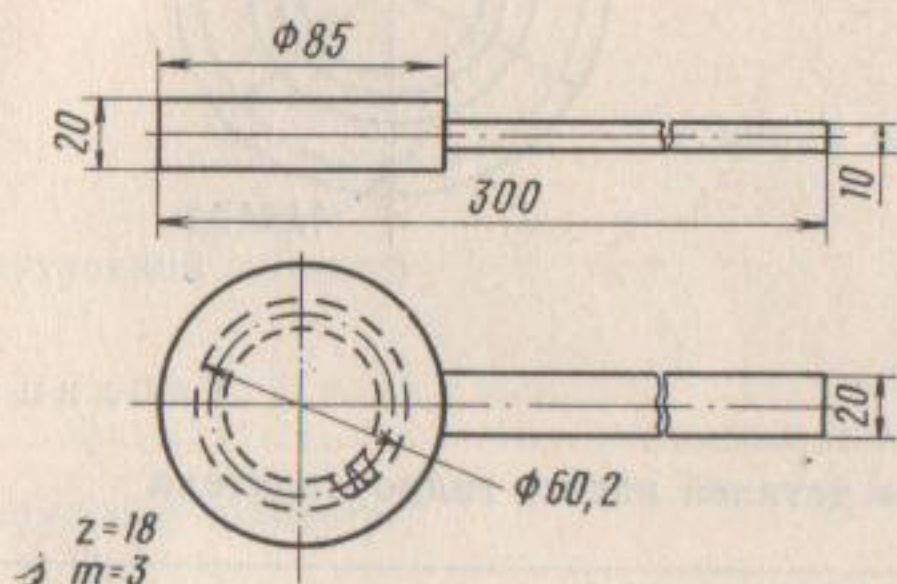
Приспособление для закрепления шестерни привода насоса рулевого управления
